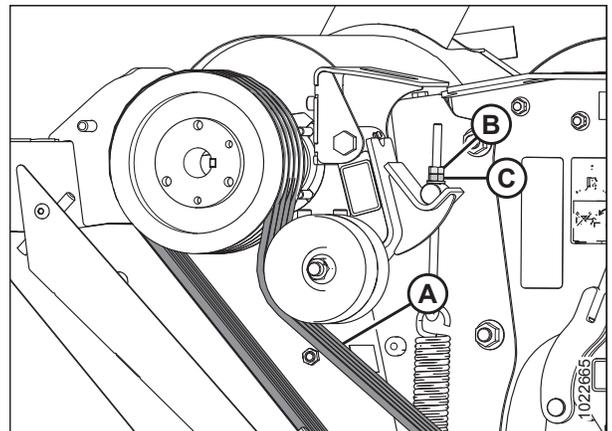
Contre-écrou et écrou de réglage du côté gauche du type tracté à disques rotatifs
